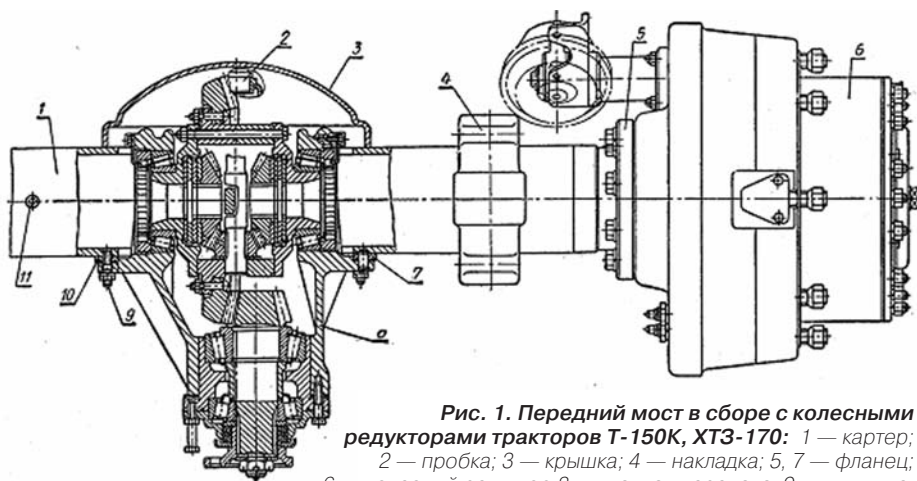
Передний мост в сборе с колесными редукторами тракторов Т-150К, ХТЗ-170: 1 — картер; 2 — пробка; 3 — крышка; 4 — накладка; 5, 7 — фланец; 6 — колесный редуктор; 8 — главная передача; 9 — шпилька; 10 — прокладка; 11 — сапун
